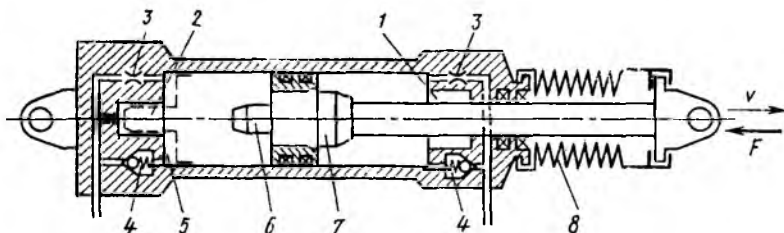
Гидроцилиндр с концевыми дроссельными тормозами и защитным штоком
